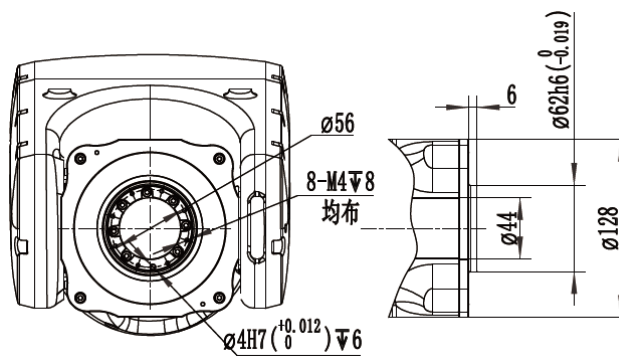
Размеры фланца CRP-RH14-10-W.
